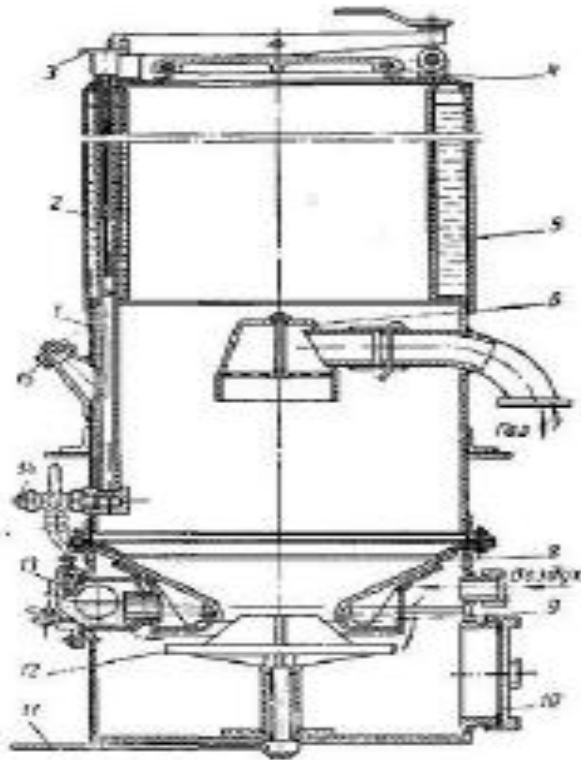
Газогенераторна установка ЦНДІАТ-АГ-2 прямого процесу газифікації: 1-корпус; 2-шуп; 3-пробка; 4-завантажувальний люк; 5-бак для води; 6-газовідбірний ковпак; 7- газовідбірний патрубок; 8-камера газифікації; 9-сорочка випарника; 10-золотниковий люк; 11 - рукоятка для шуровки; 12поворотна плита; 13поплавкова камера; 14-триходовий кран; 15-горловина для шуровки ломом.
